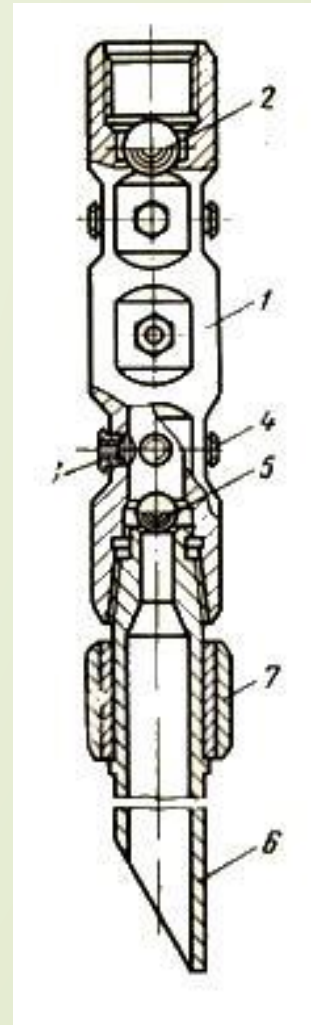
Аппарат для ГПП АП-6М: 1 - корпус; 2 - шар опрессовочного клапана; 3 - узел насадки; 4 - заглушка; 5 - шар клапана; 6 - хвостовик; 7 - центратор
